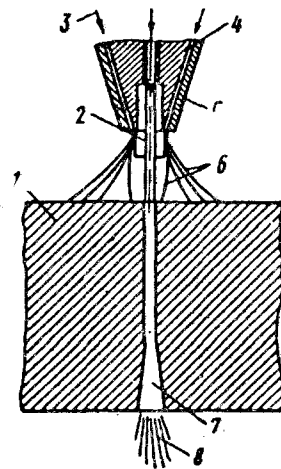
Газокислородная резка: 1 — разрезаемый металл; 2 — струя режущего кислорода; 3 — горючая смесь; 4 — режущий мундштук; 5 — мундштук подогревающего пламени; 6 — подогревающее пламя; 7 — рез; 8 — шлаки
